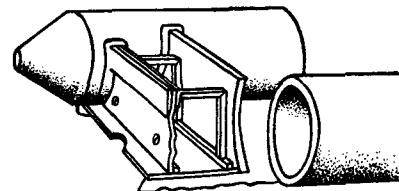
Транец с дополнительной жесткой герметизирующей перегородкой
